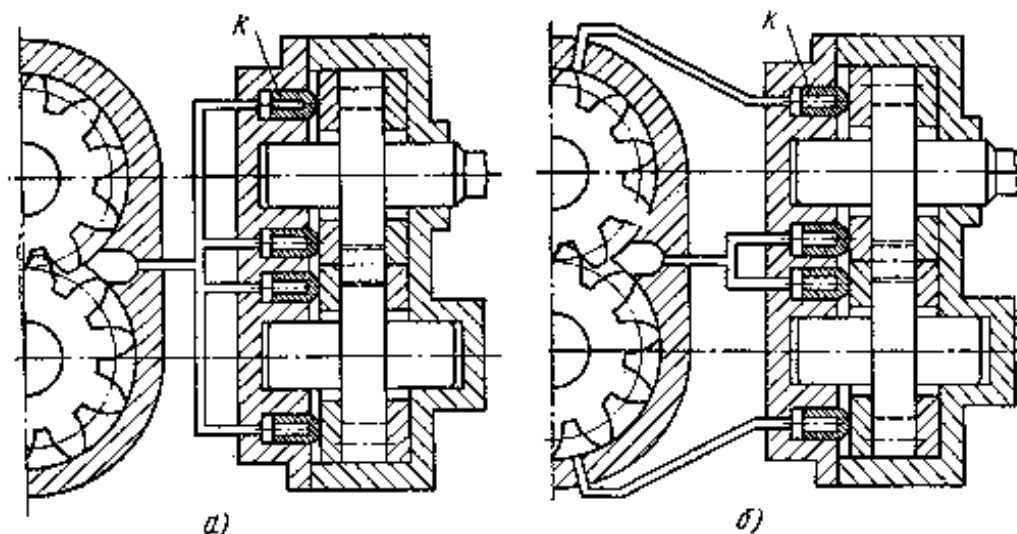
Схемы обеспечения равномерной нагрузки шестерен по торцам
